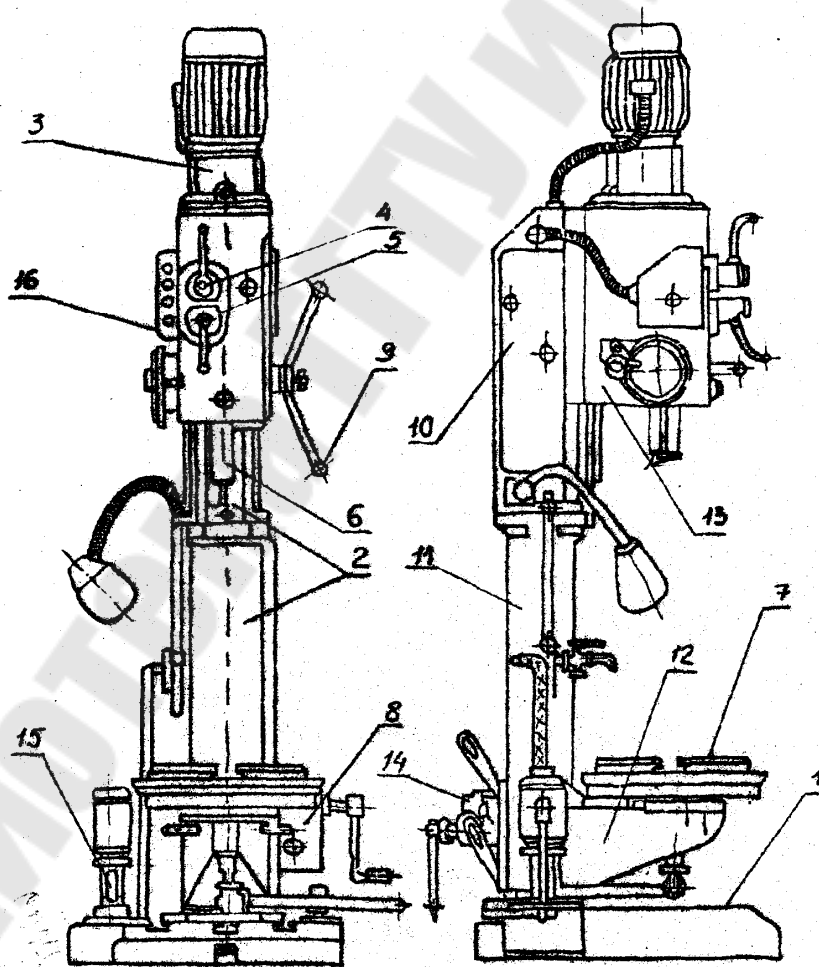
Общий вид вертикально-сверлильного станка модели 2H125Л
